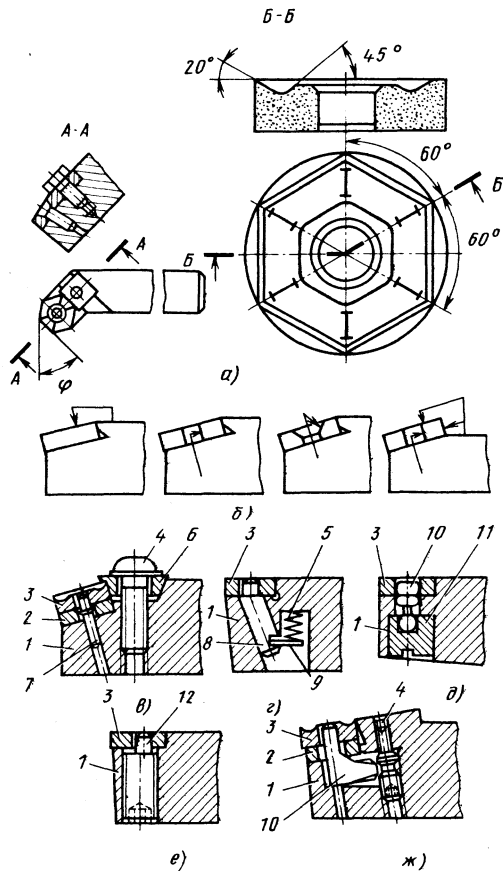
Типовые конструкции пластин и устройств механического крепления
